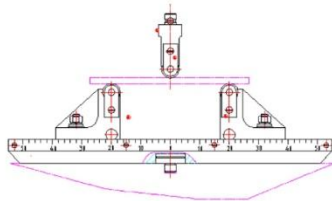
Identador y apoyos de viga para ensayo de flexión.
